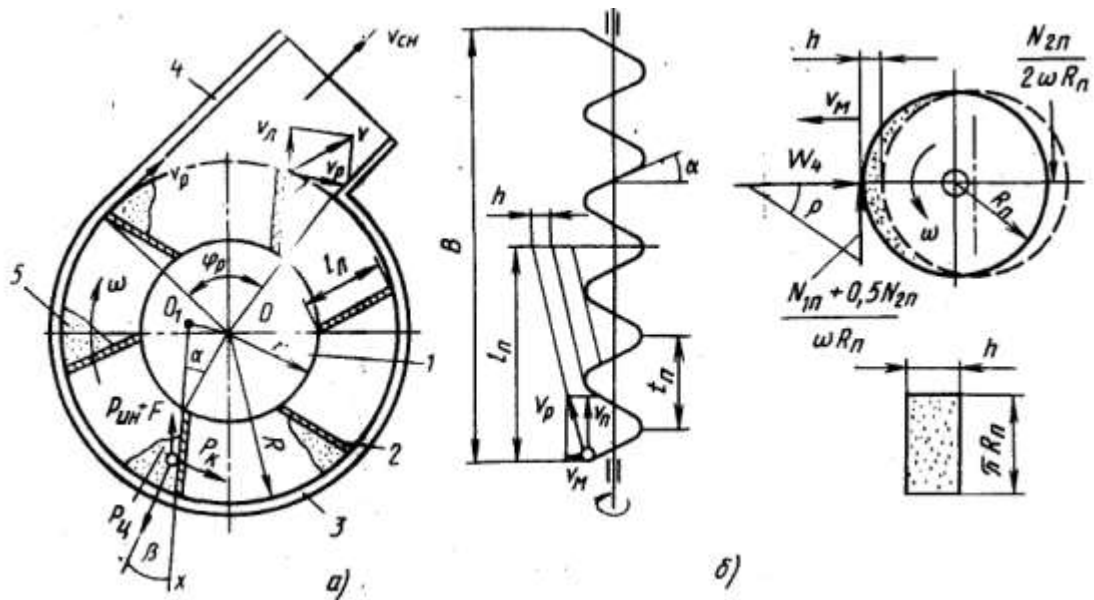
Схема взаємодії з снігом: а – роторно-лопатевого металельника; б – шнекового та фрезерного живильників; 1 - маточина ротора; 2 – лопата; 3 – нерухомий кожух; 4 – викидний патрубок; 5 – призма волочіння снігу перед лопатею
